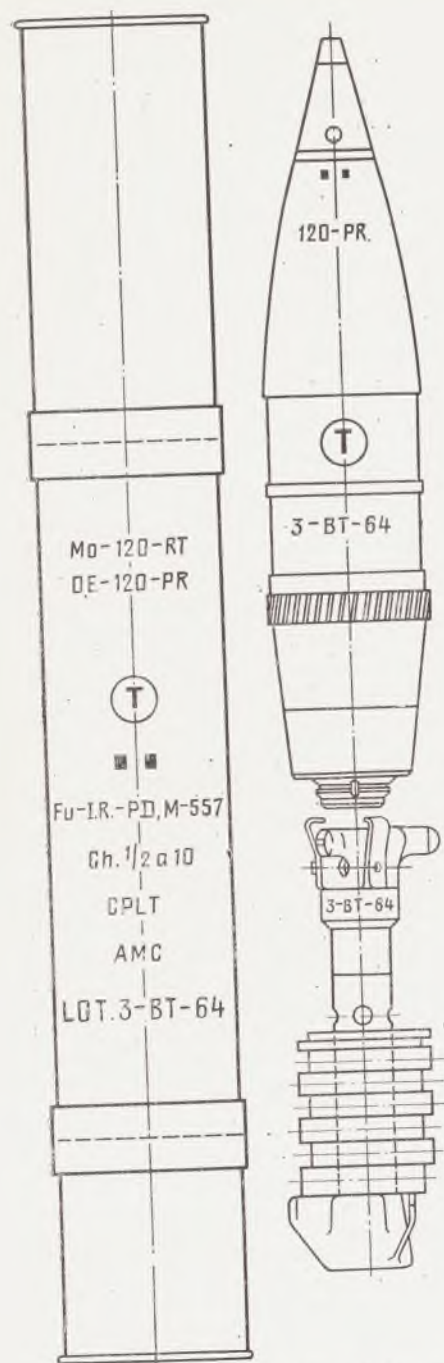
Образец маркировки ОФ снаряда PR.14 и укупорки для выстрела
